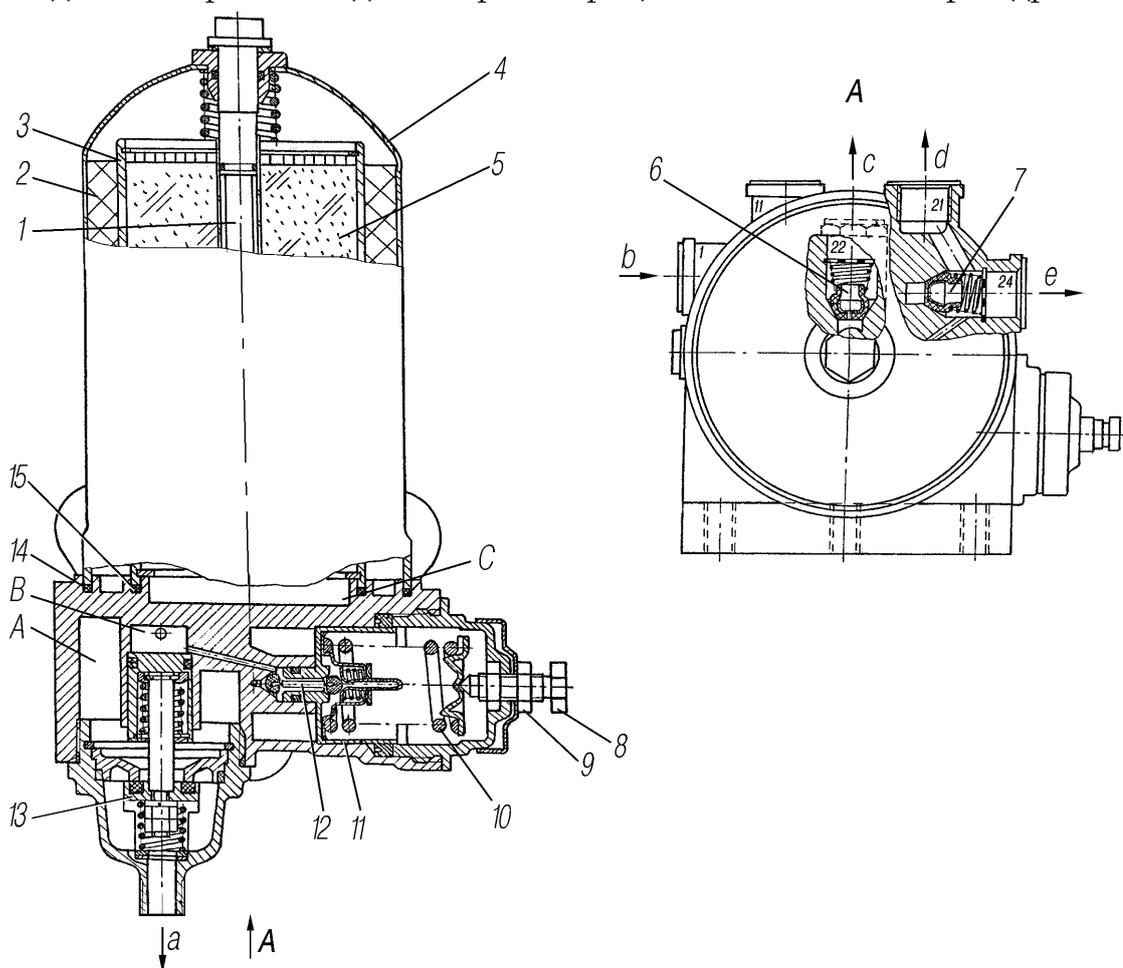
Влагомаслоотделитель со встроенным регулятором давления: 1-винт; 2-фильтр; 3-стакан; 4-колпак; 5-элемент адсорбирующий; 6-дроссель; 7-клапан обратный; 8-винт регулировочный; 9-контргайка; 10-пружина; 11-уравновешивающий поршень; 12-клапан впускной; 13-клапан разгрузочный; 14,15-уплотнительные кольца; А,В,С-полости; а-вывод в атмосферу; b-подвод от компрессора; с-вывод в регенерационный баллон; d,e-вывод в систему
